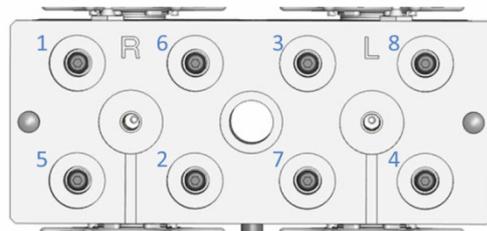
Ordre de serrage des vis de la plaque de rinçage des joints
